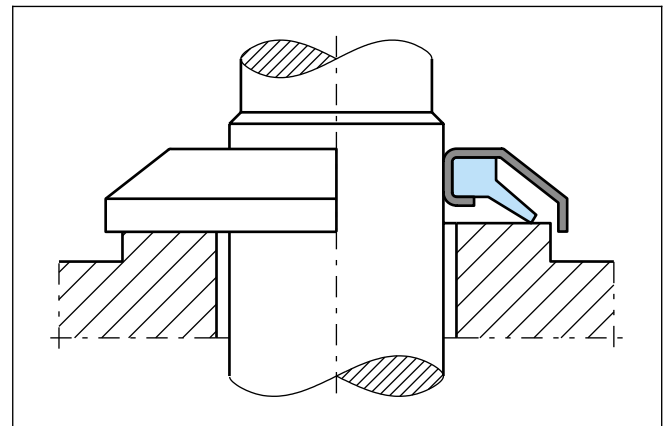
Ausführung der Lauffläche für senkrechte Wellen
